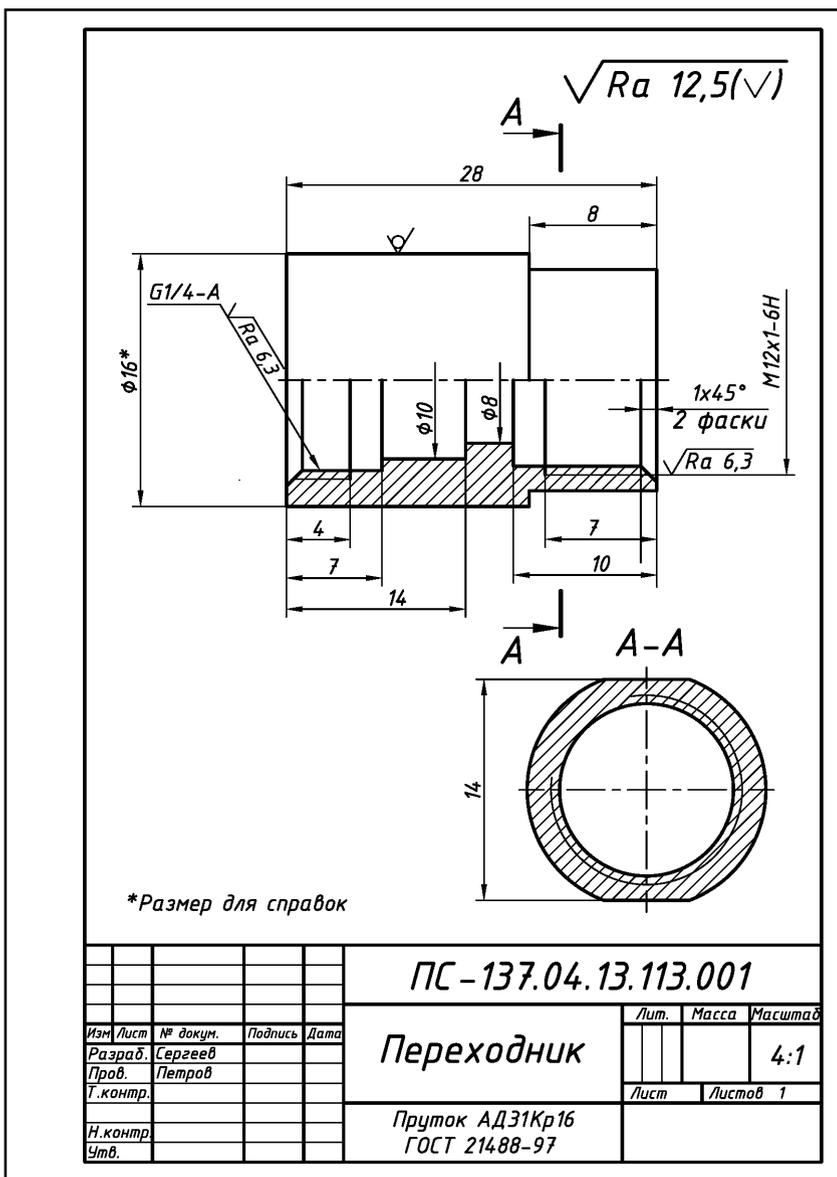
Оформление рабочего чертежа точеной детали из металла
